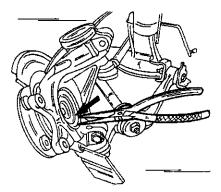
Снятие стопорного кольца с задней стороны поворотного кулака (на рисунке показан установленный поворотный кулак).
